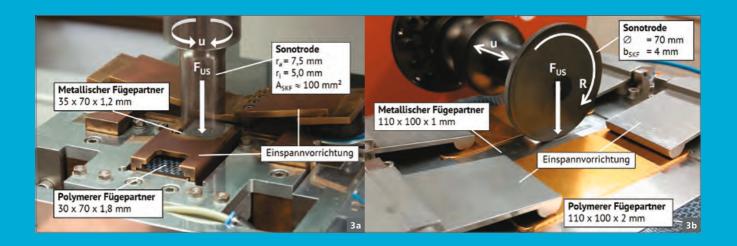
Ultraschallschweißsysteme für Metall/CFK-Verbunde: a) Torsionsschweißsystem der Fa. Telsonic Ultrasonics b) Rollnahtschweißsystem für ebene Hybridstrukturen der Fa. Branson Ultraschall.
